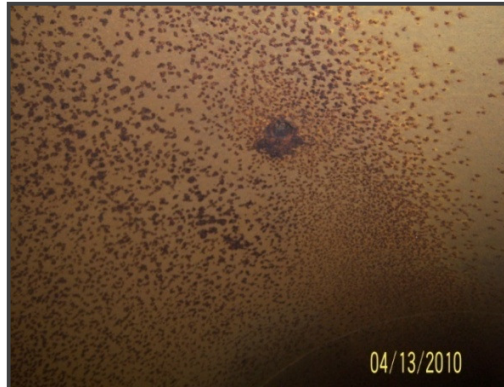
Cordón de soldadura con presencia de corrosión por picadura.
